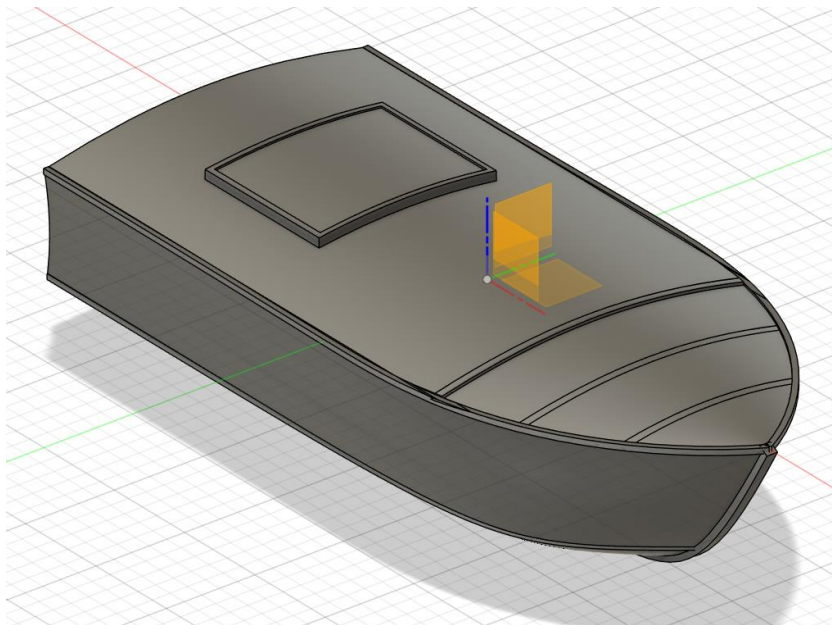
Зовнішній вигляд корпусу з обшивкою
